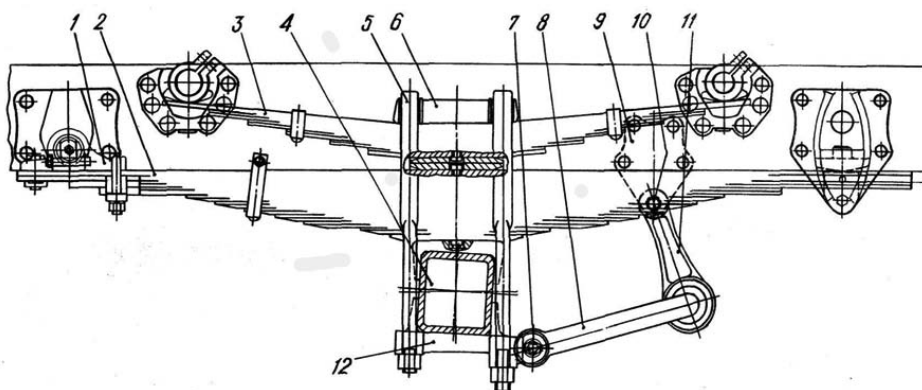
Задняя подвеска двухосных автомобилей: 1 — накладное ушко рессоры; 2 — рессора; 3 — дополнительная рессора; 4 — балка заднего моста; 5 — стремянка; 6 — накладная рессоры; 7 — гайка; 8 — вал стабилизатора поперечной устойчивости; 9 — кронштейн; 10 — палец; 11 — рычаг; 12 — кронштейн
